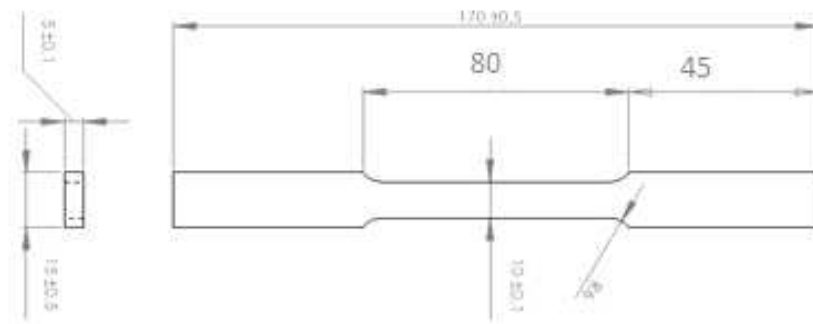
Dessin de définition de l'éprouvette plate
